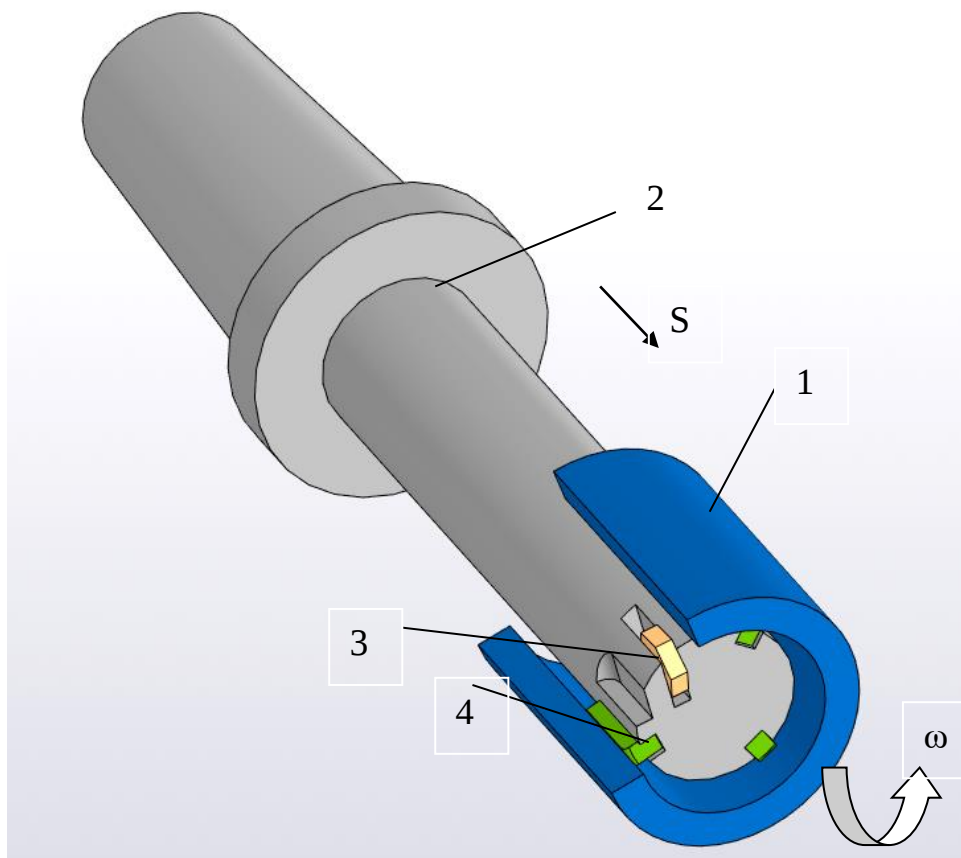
Схема процесу розточування отвору розточною оправкою із ріжучою пластиною та напрямними опорами
